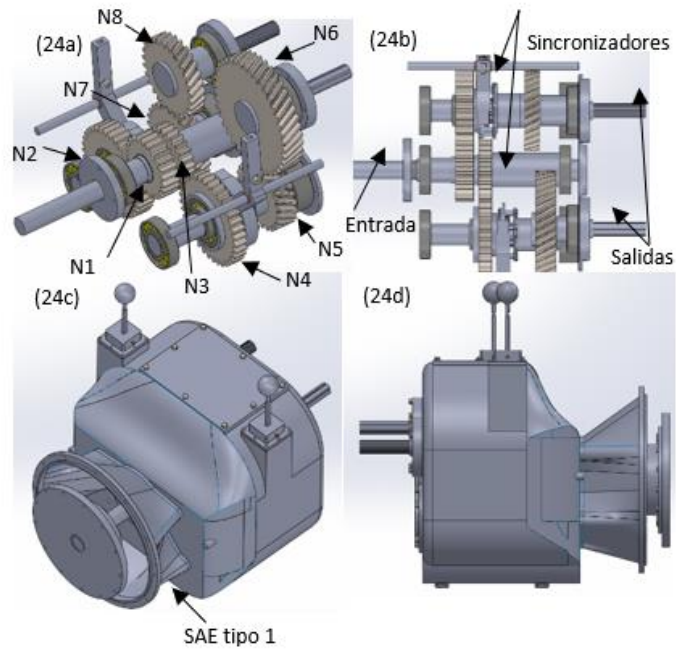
(a) vista del tren de engranaje de la transmisión; (b) vista superior del tren de engranes; (c) vista isométrica; (d) vista lateral.
